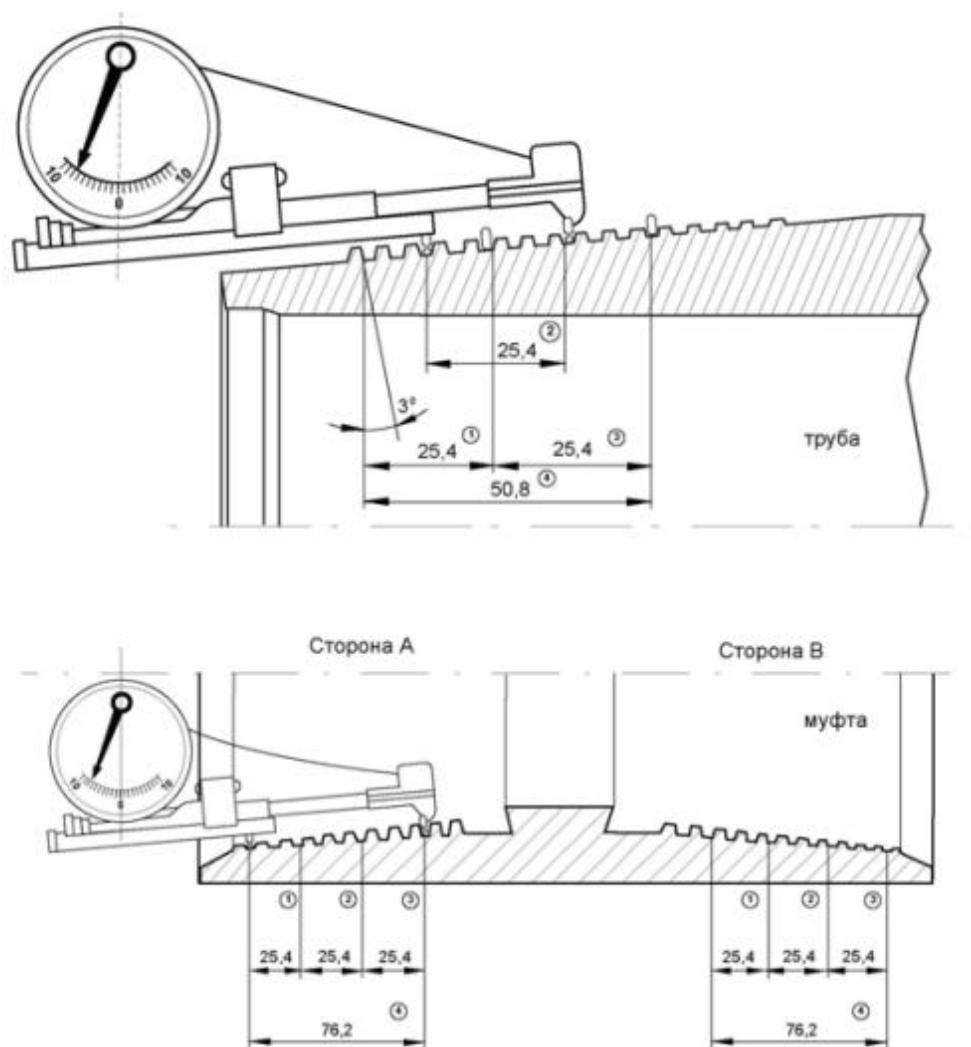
Измерение отклонения шага резьбы труб и муфт
